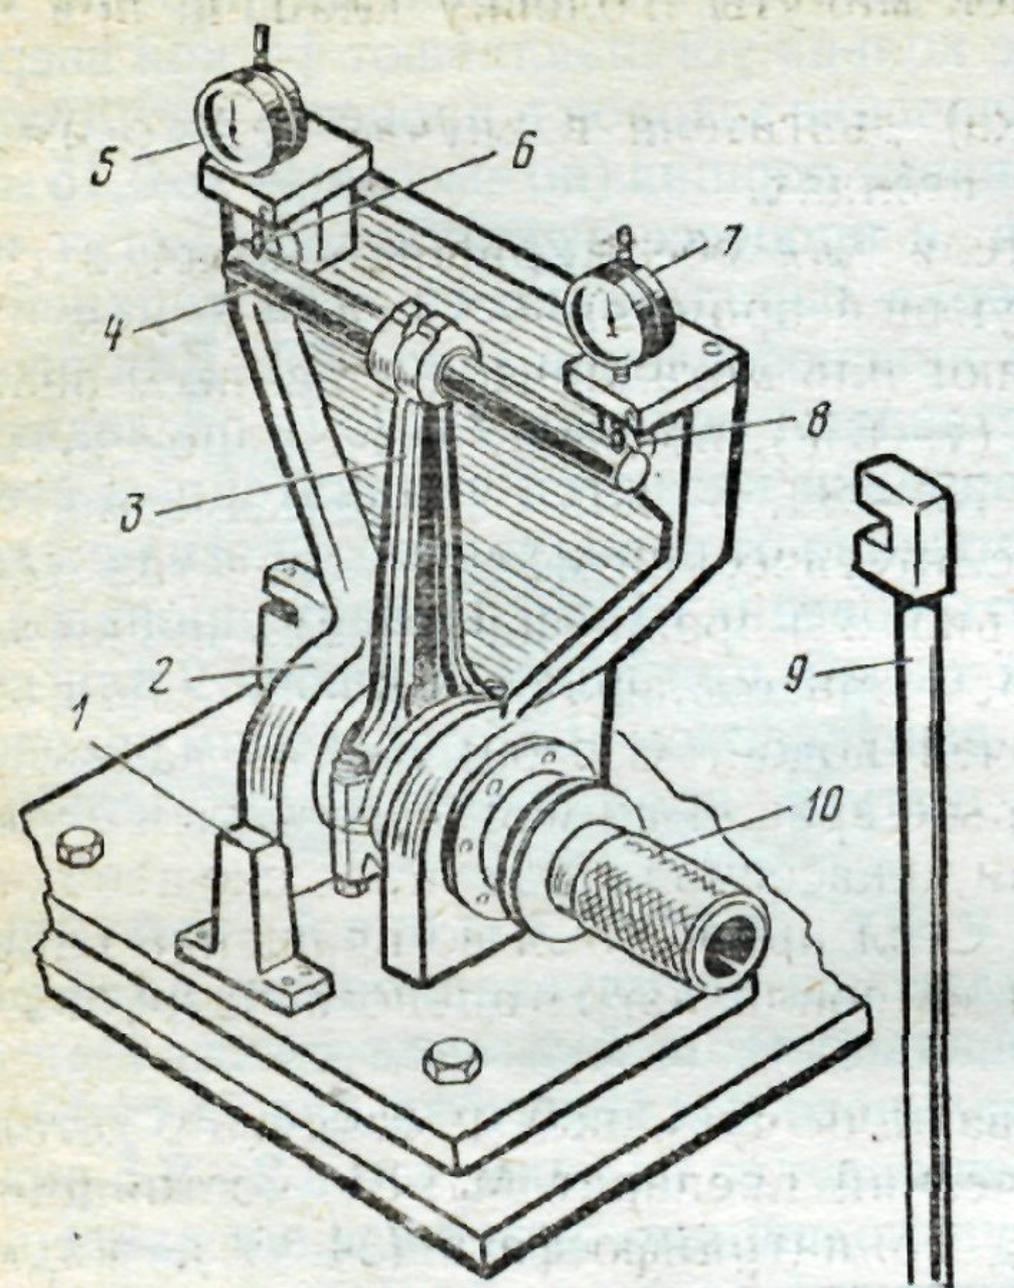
Приспособление для проверки соосности верхней и нижней головок и правки шатуна:
